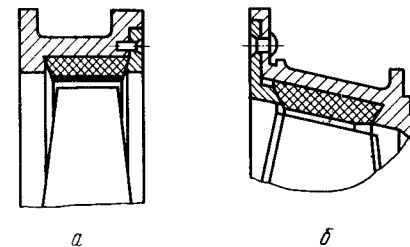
Металлокерамические вставки в корпусе турбин:
